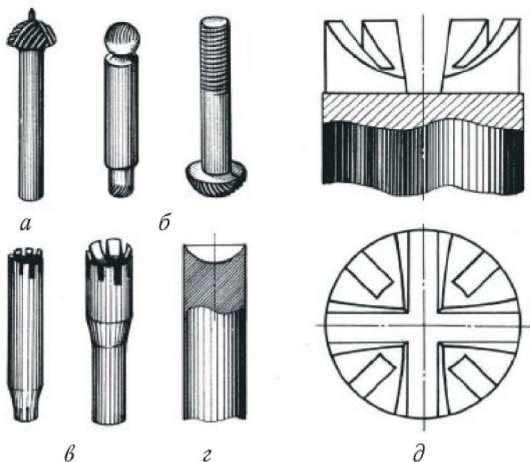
Фрезы для обработки сферических поверхностей (шарошки):
